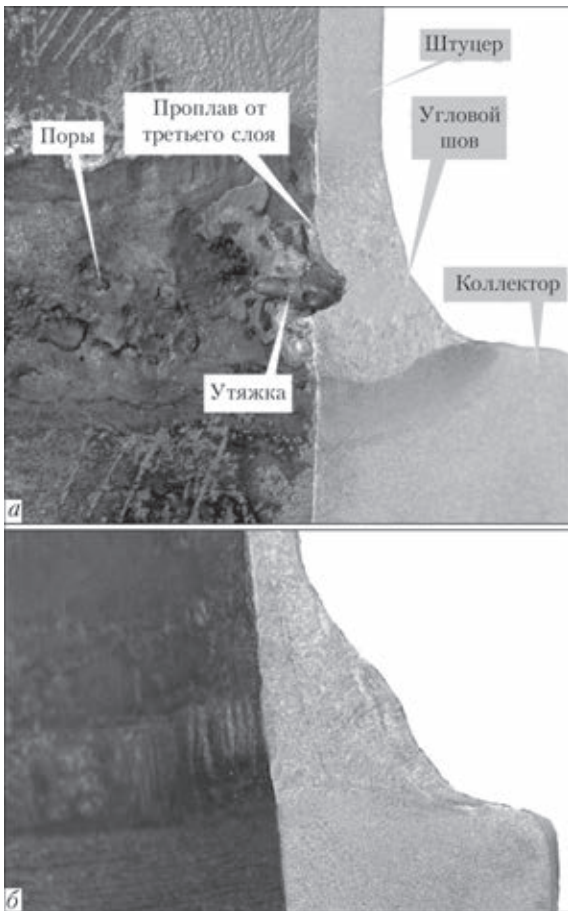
Угловые сварные соединения штуцера с коллектором: *a* — поперечное сечение соединения с дефектами в корневом валике, выполненного без поддува аргона; *б* — поперечное сечение соединения, выполненного с поддувом аргона
